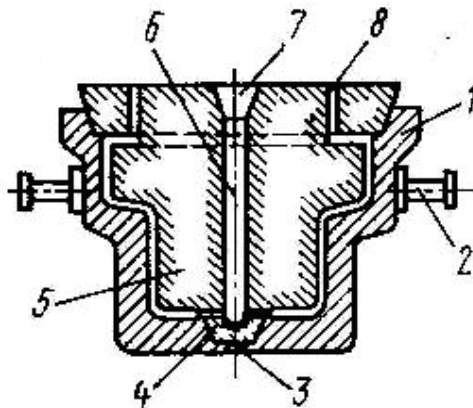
Конструкция вытряхного кокиля для алюминиевой отливки:
